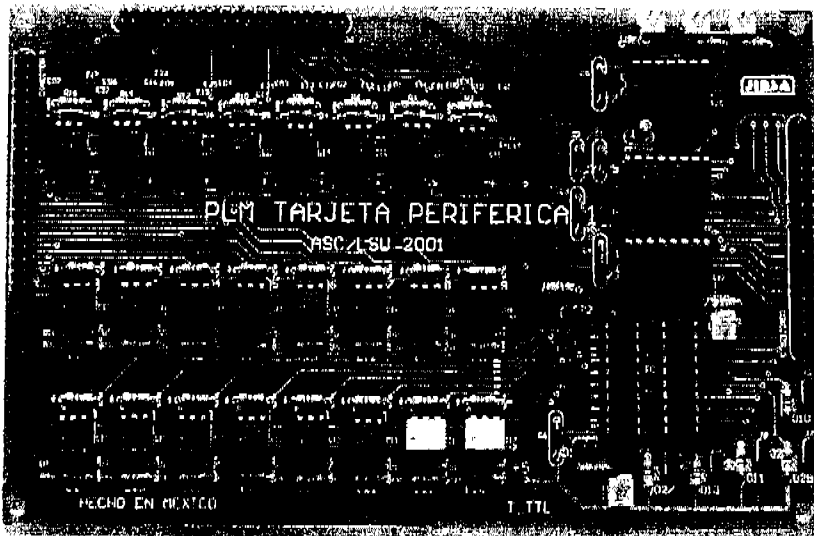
Fotografía de la Tarjeta Periférica I terminada.
